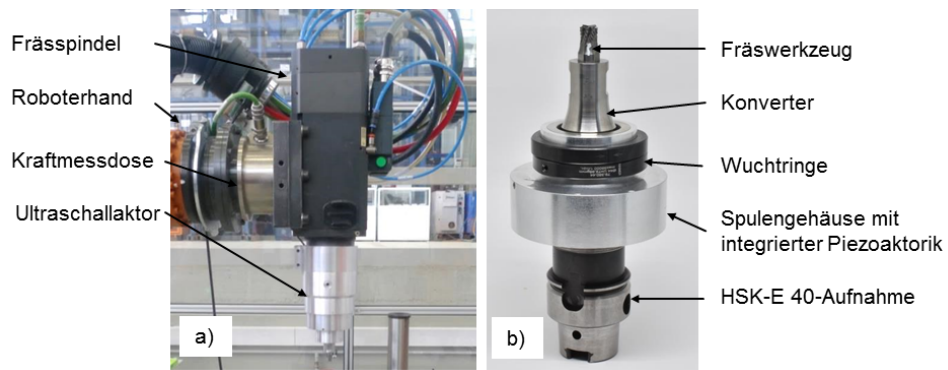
Ultraschall-Aktorsystem mit Fräs Werkzeug
